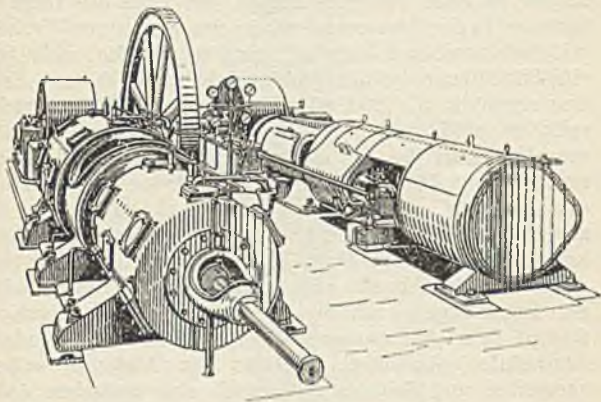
Schmidt-Borsig-Hochdruckvorschaltmaschine für 60 at Anfangsdruck und 10—12 ata Gegendruck (rechte Maschinenseite)
